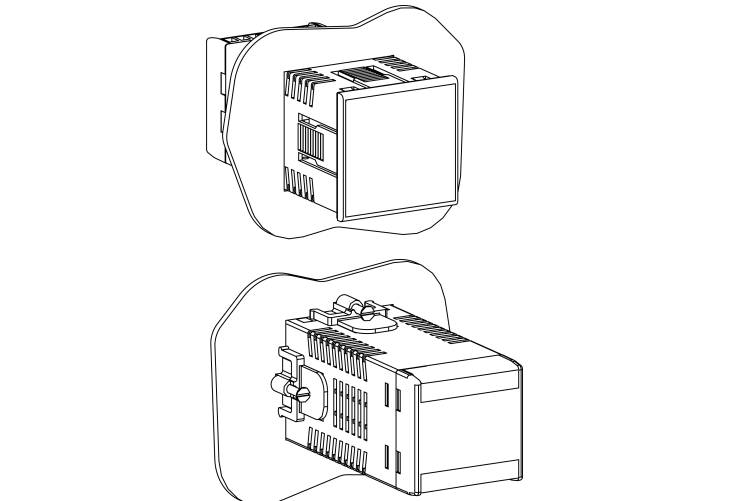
Монтаж прибора щитового крепления Щ5
